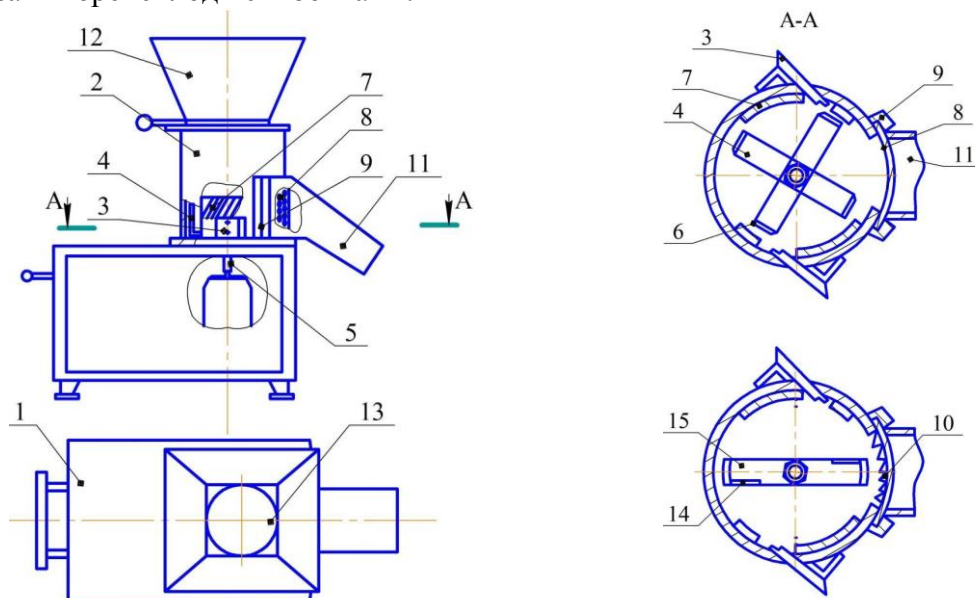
Універсальний подрібнювач кормів: 1 – основа; 2 – дробильна камера; 3 – бічні ножі; 4 – хрестоподібний ніж; 5 – вал; 7 – знімні накладки; 8 – змінні решета; 9 – напрямні; 10 – шатківниця; 11 – знімний рукав; 12 – знімний бункер; 13 – шибера; 14 – знімний ніж; 15 – додаткові вертикальні ребра.
